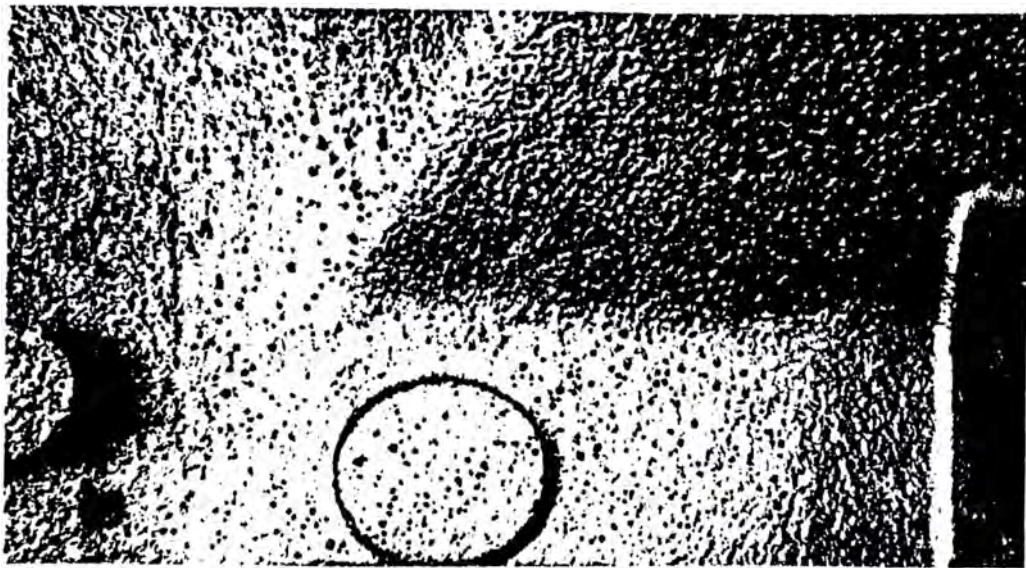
Pinholes sobre la parte superior de una carcasa, producida en fundición nodular.
